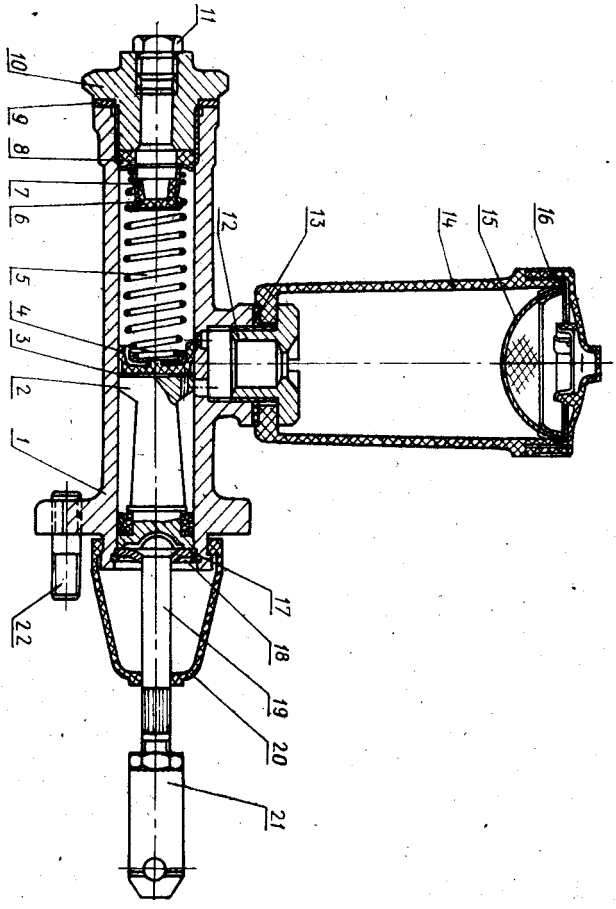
Главный цилиндр тормоза: 1 — корпус главного цилиндра; 2 — поршень; 3 — клапан; 4 — манжета уплотнителя; 5 — прокладка; 6 — клапан; 7 — обойма клапана; 8 — кольцо упорное; 9 — прокладка штока; 10 — штифт главного цилиндра; 11 — пробка; 12 — штифт бачка; 13 — прокладка штока; 14 — корпус бачка; 15 — сетка; 16 — крышка бачка; 17 — шайба упорная; 18 — кольцо упорное; 19 — толкатель; 20 — колпак защитный; 21 — вышка толкателя; 22 — шпилька.
